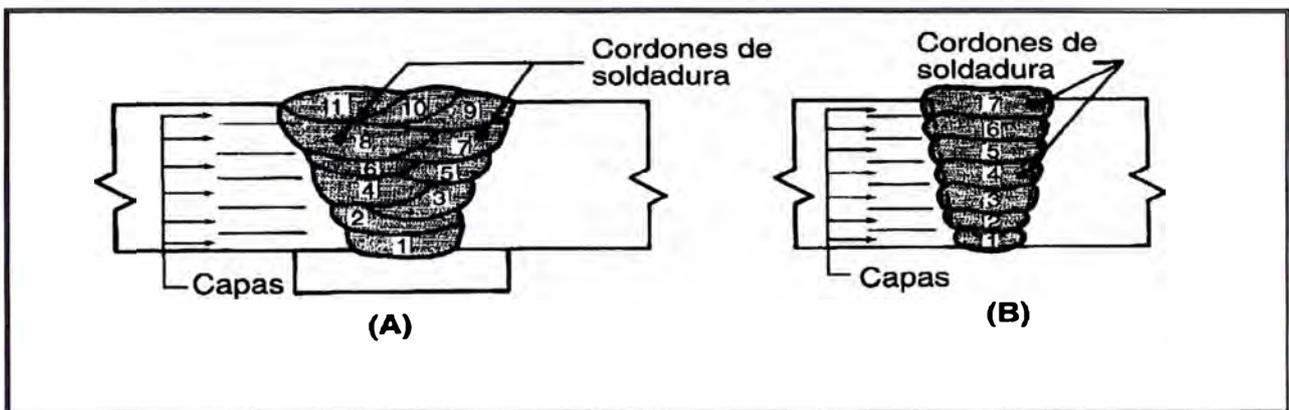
Cordones de Soldadura y Capas de Soldadura
